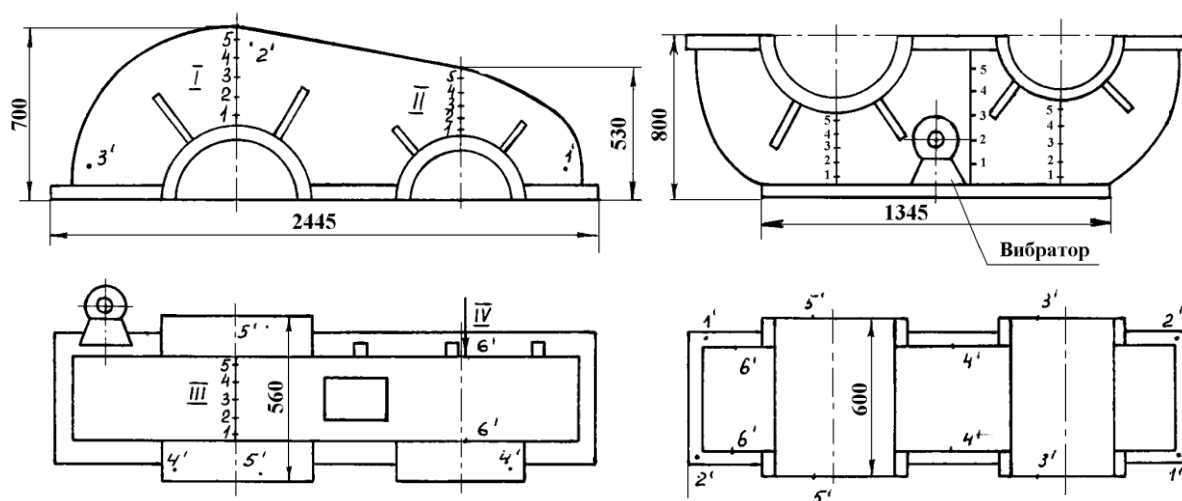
Схема розташування базових точок виміру деформацій на кришці і корпусі редуктора (б)
